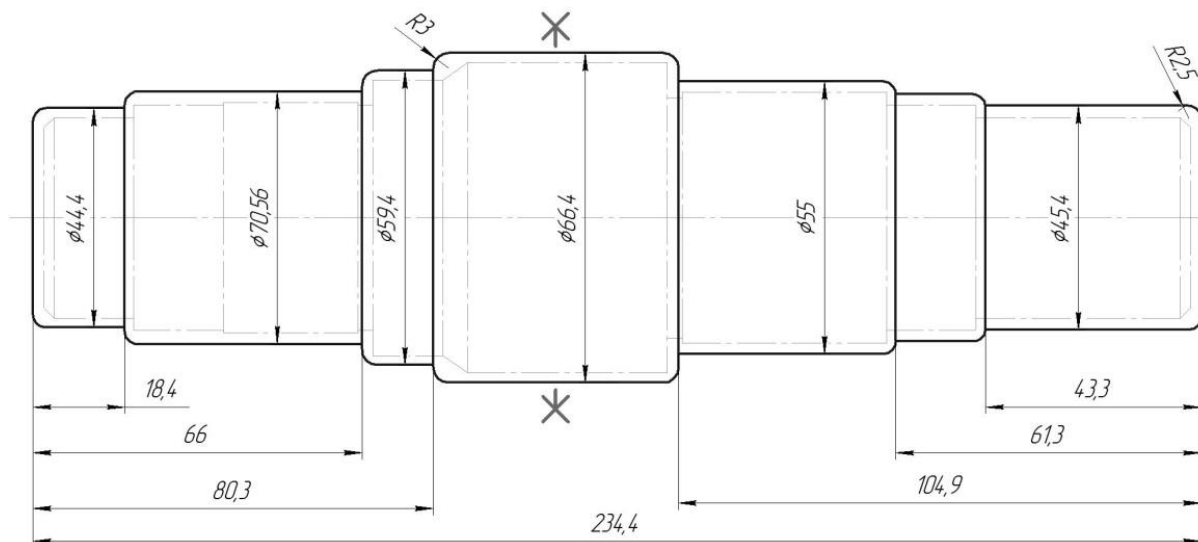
Ескіз заготовки для кування на ГKM
